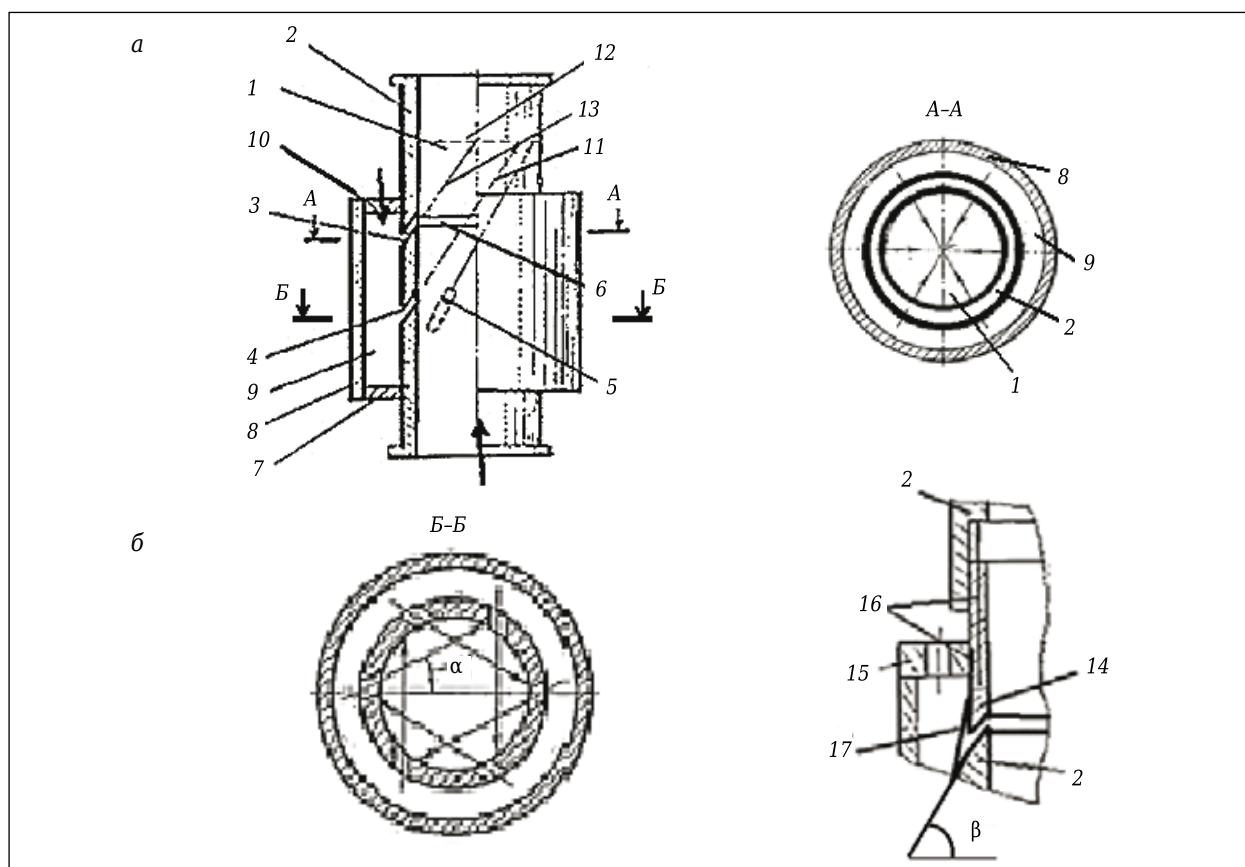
Схема подъемного устройства: а — общий вид устройства; б — узел резьбового крепления кольцевого патрубка 14 к фланцу 15 секции 7 нагнетания воздуха. Остальные обозначения — в тексте
